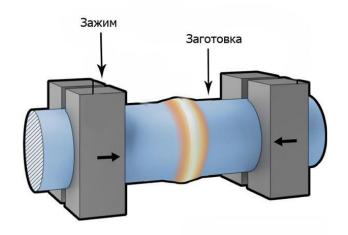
Деформация металла при контактной сварки деталей
